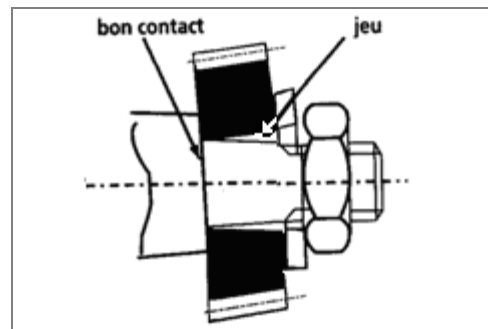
Cas d'un assemblage plan prépondérant avec défaut
